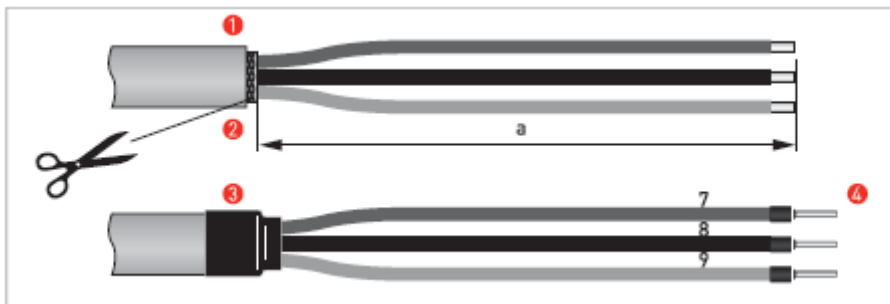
Подготовка кабеля тока возбуждения для измерительного датчика
